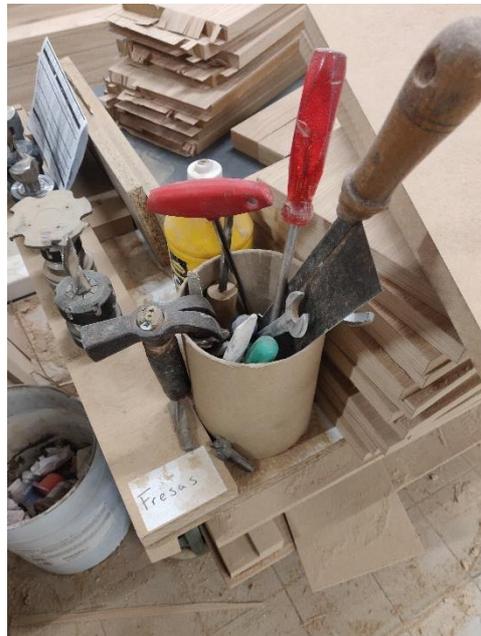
Rotulagem do local de armazenamento segundo o tipo de artigo (Máquina de cola e prensa quente)
